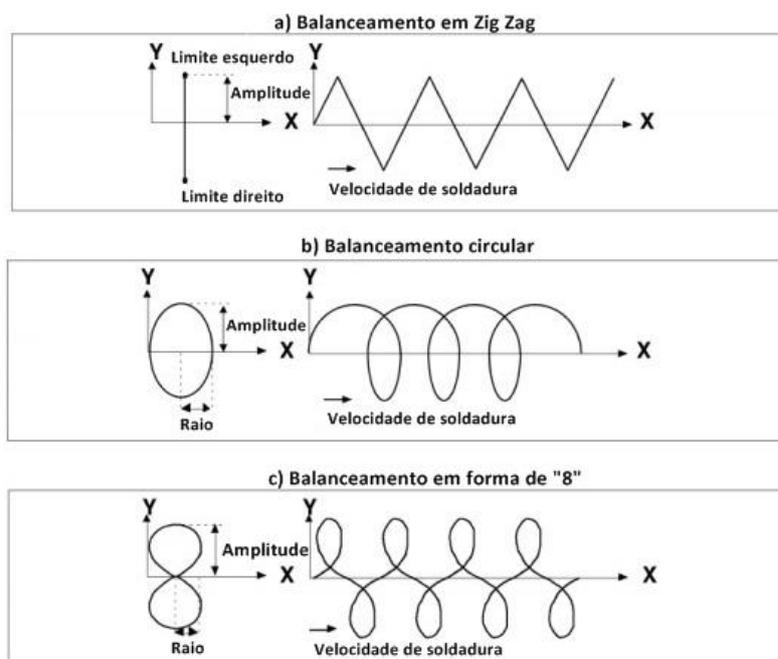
Exemplo de movimentos *de* balanceamento de soldadura. Adaptado de:
